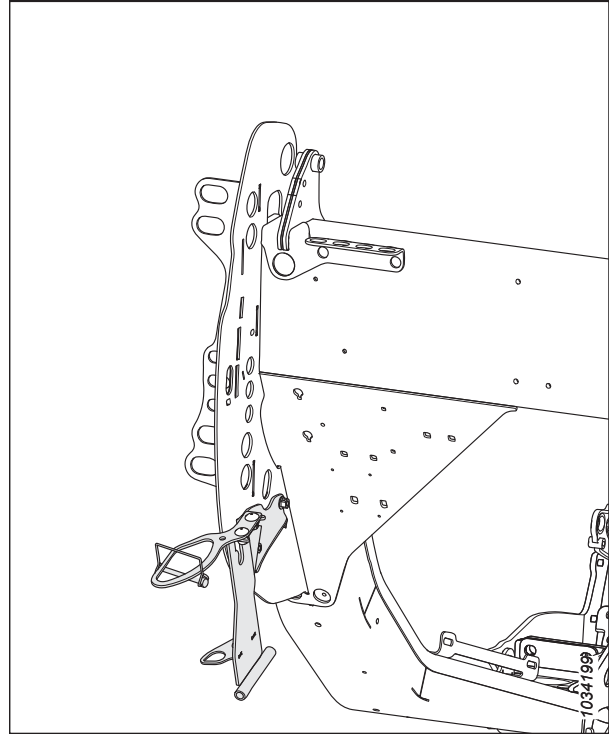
Souprava úložného držáku pro děliče – MACB7030
